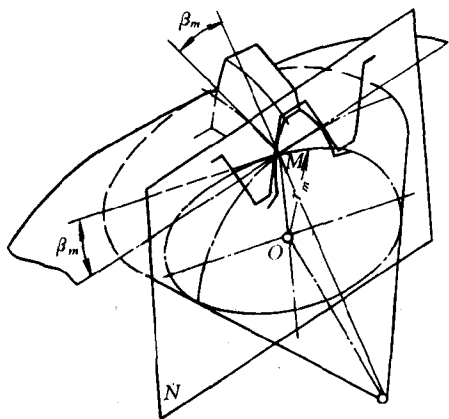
曲齿锥齿轮当量齿轮的切齿啮合
